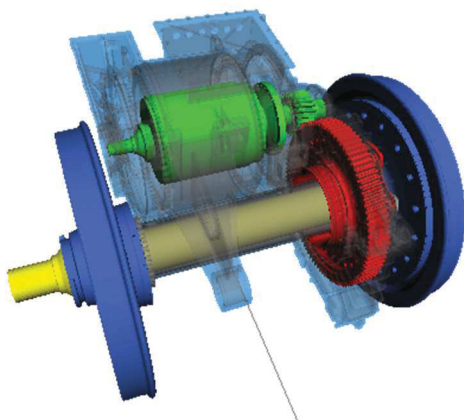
Detail kompenzace relativních pohybů mezi motorem a převodovkou. [17]
